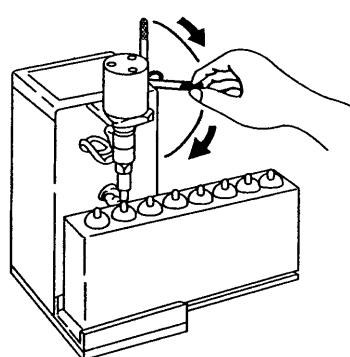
Soudage de tubes d'étanchéité
